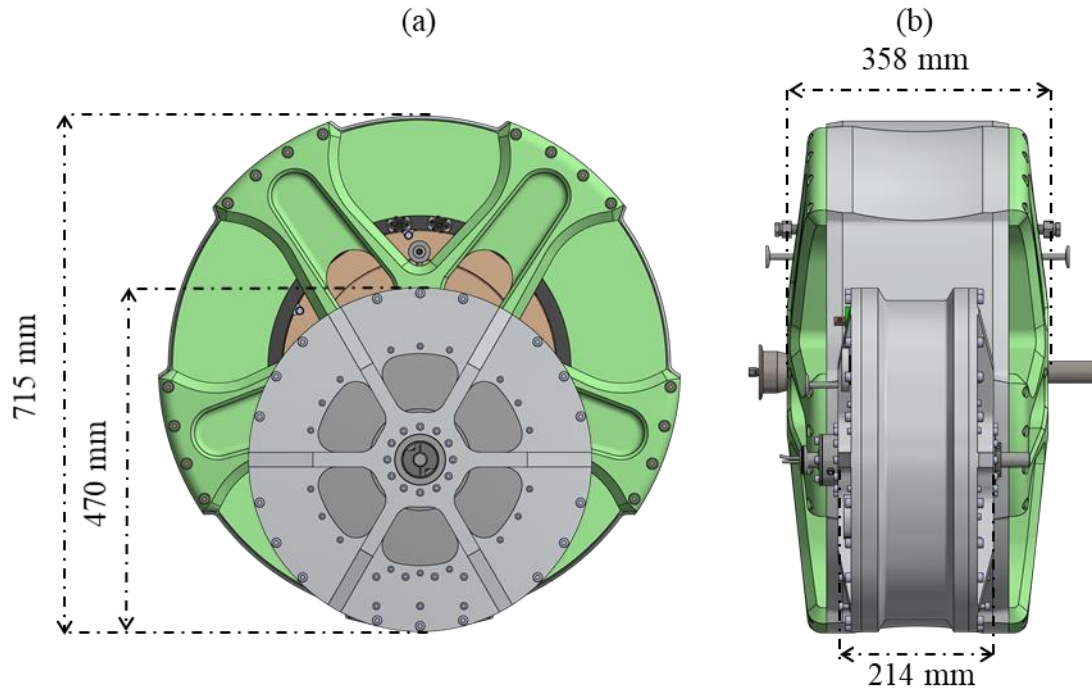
Comparaison des dimensions du démonstrateur FROST et du prototype RESUM. (a) Vue de face. (b) Vue latérale.
